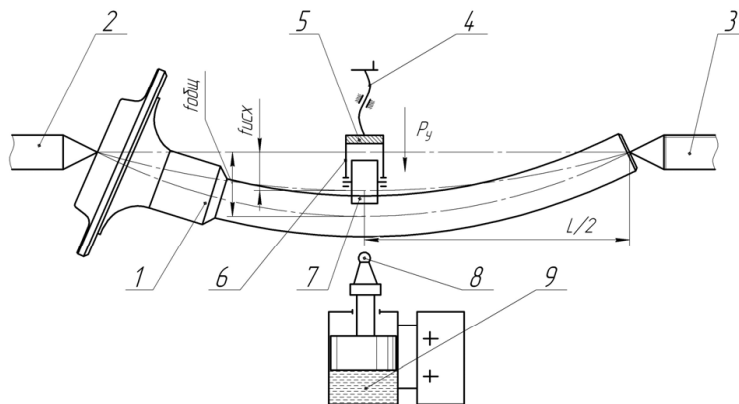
Схема правки полуоси автомобиля поверхностным пластическим деформированием с одновременной отделочно-упрочняющей обработкой поверхности: 1 – восстанавливаемое изделие; 2, 3 – центры станка; 4 – винтовая пара; 5 – каретка; 6 – призма; 7 – сглаживающие ролики; 8 – упрочняющий шар; 9 – гидроцилиндр
